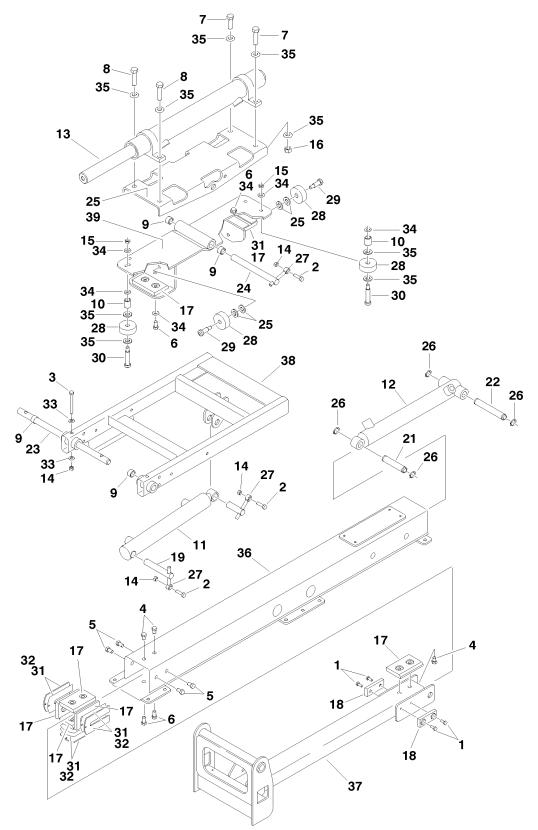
Disegno dei componenti di montaggio di Easi-Cladder™ Plus
